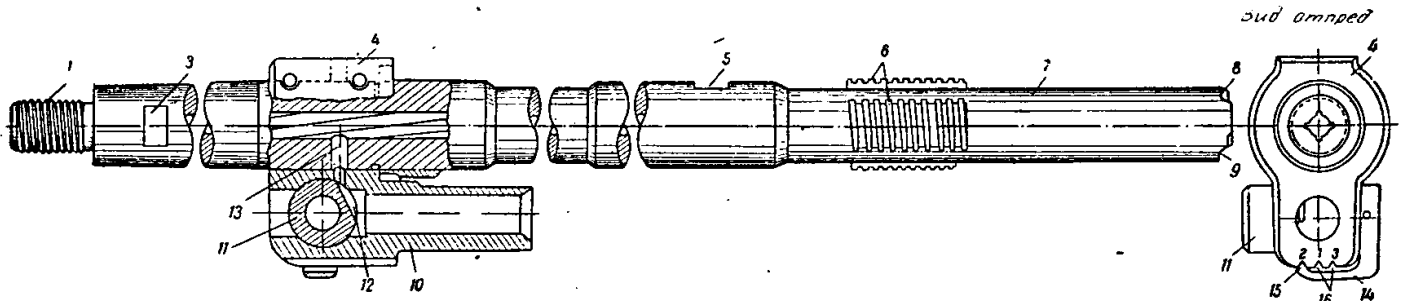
Цев, газова камера и регулатор (сб. 25):
